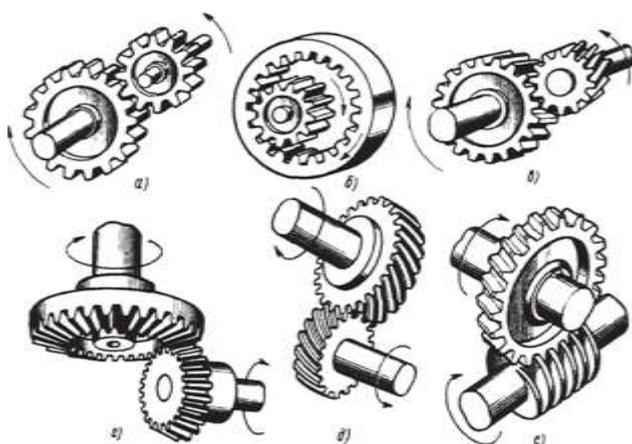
Зубчатые передачи (а-е) для вращательных движений
